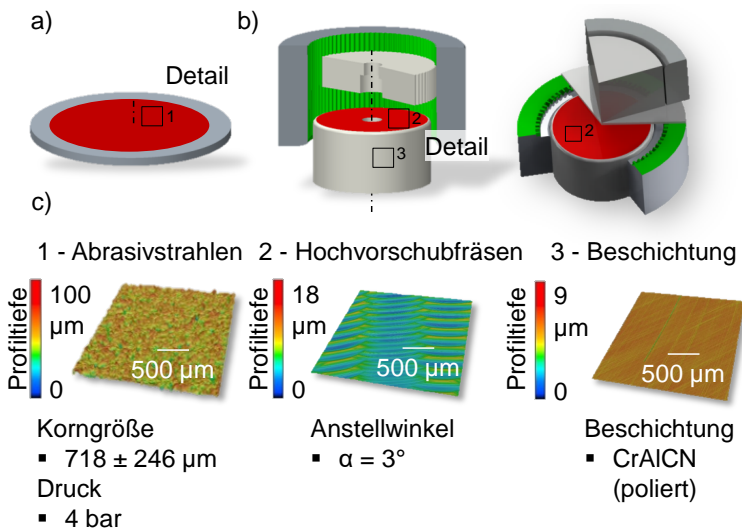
Detailansicht der Positionen a) platinen- und b) werkzeugseitiger Modifikationen und c) die ausgewählten maßgeschneiderten Oberflächen
